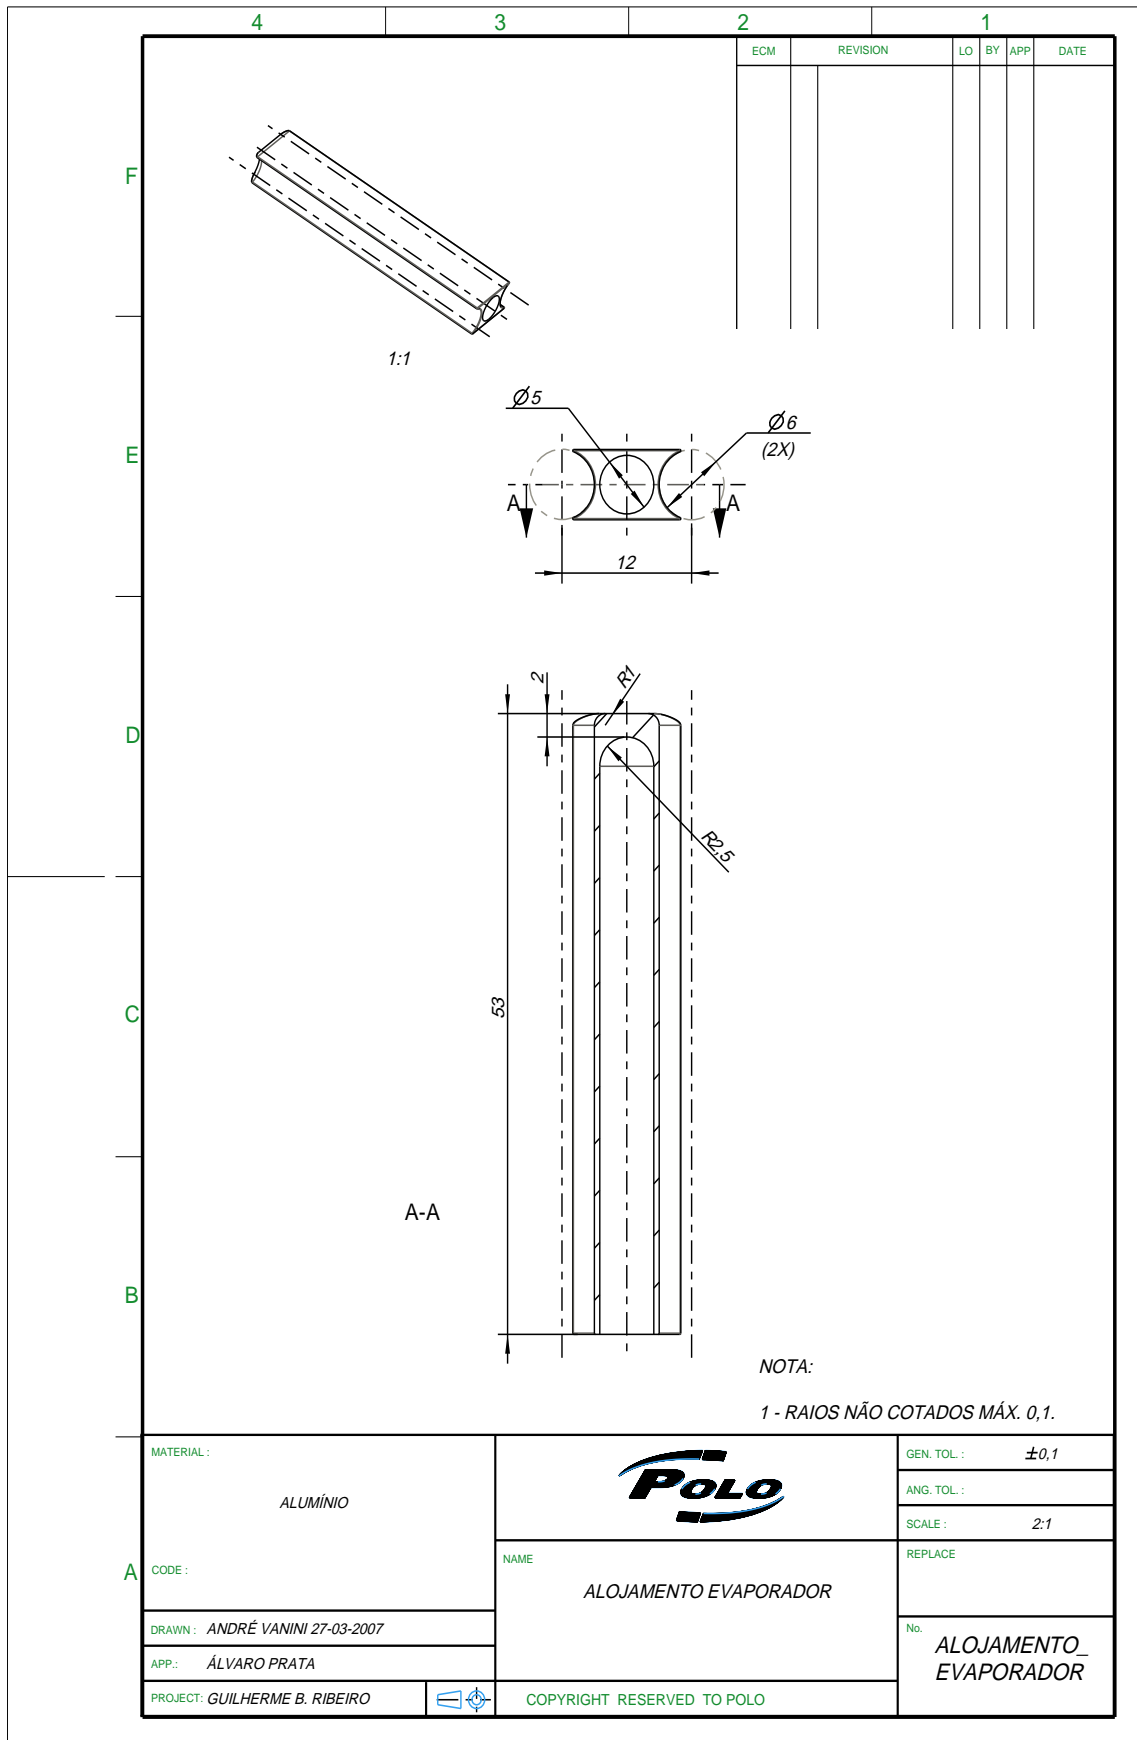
Desenho técnico do evaporador acoplado a tubos de calor - Parte II
